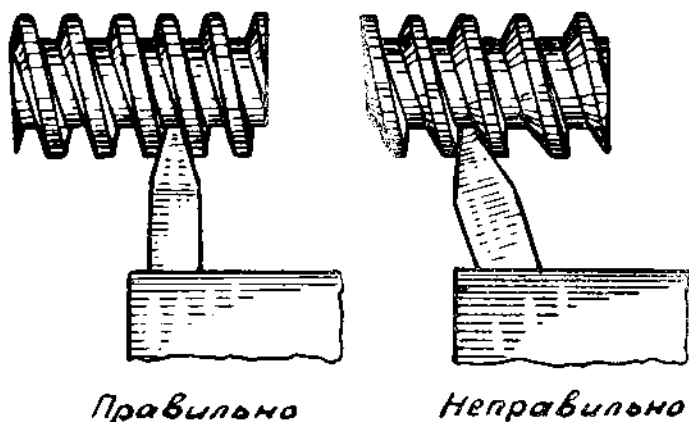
в. Резьбовые резцы токаря Бирюкова
